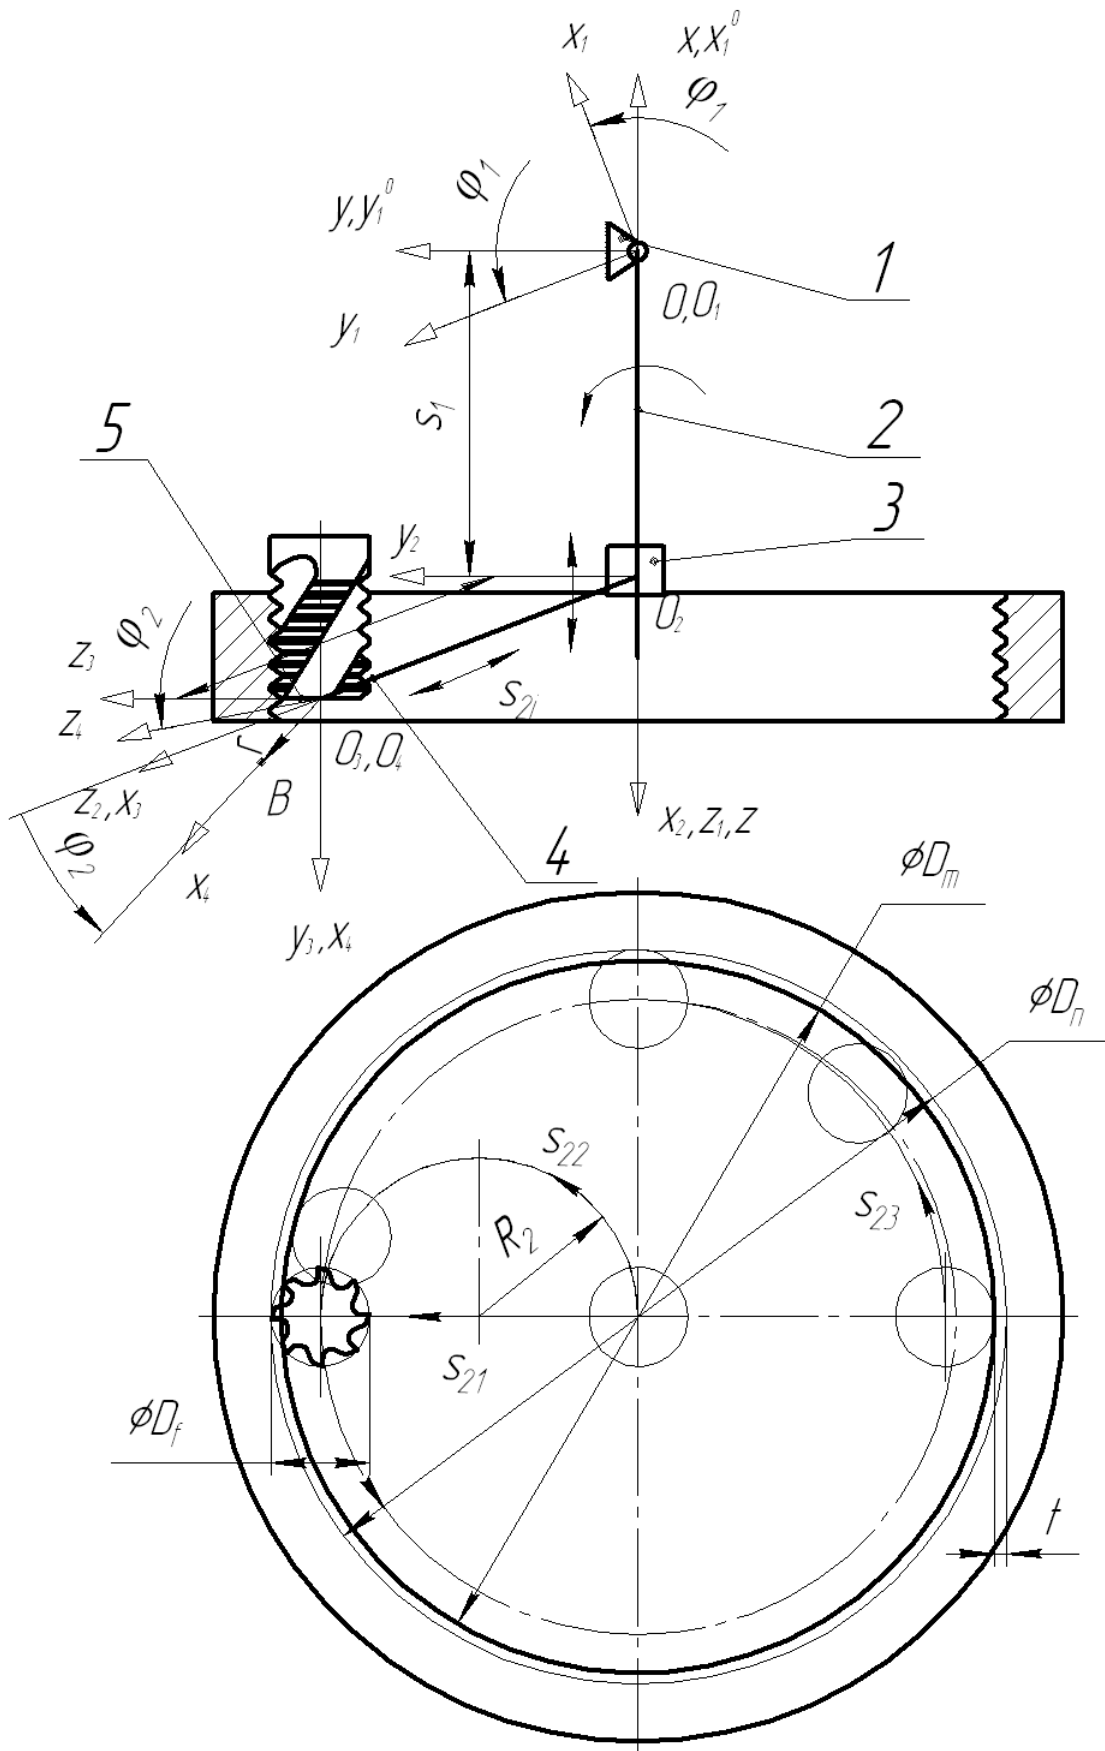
Розрахункова схема для визначення параметричного рівняння траєкторії руху вершини зуба фрези відносно поверхні отвору заготовки
